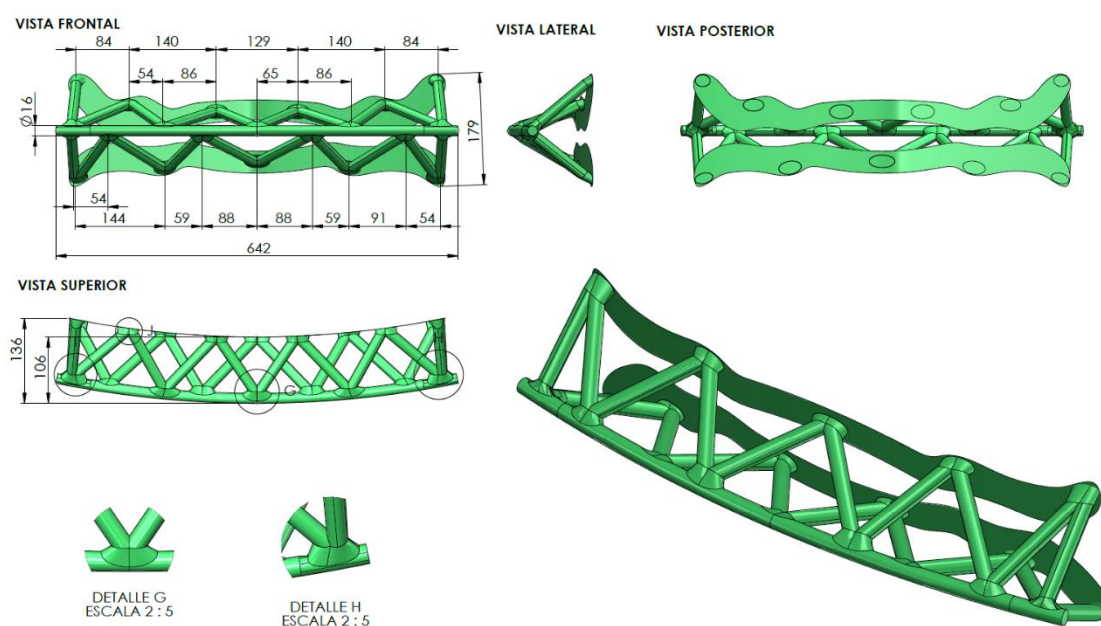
Dimensiones de probeta para ensayo de compresión, largo 642 mm, ancho máx. 136 mm, alto 179 mm
